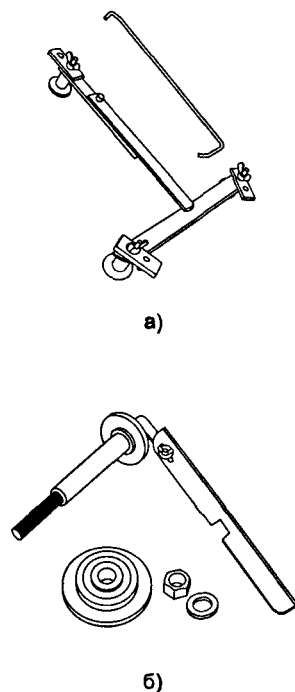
Специальный инструмент: а — съемник переднего фланца барабана; б — приспособление для демонтажа подшипников и сальника
